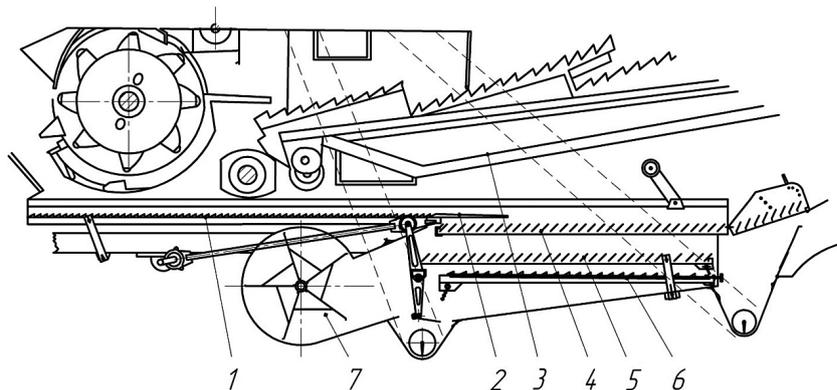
Воздушно-решётная очистка «Нива-Эффект»:
